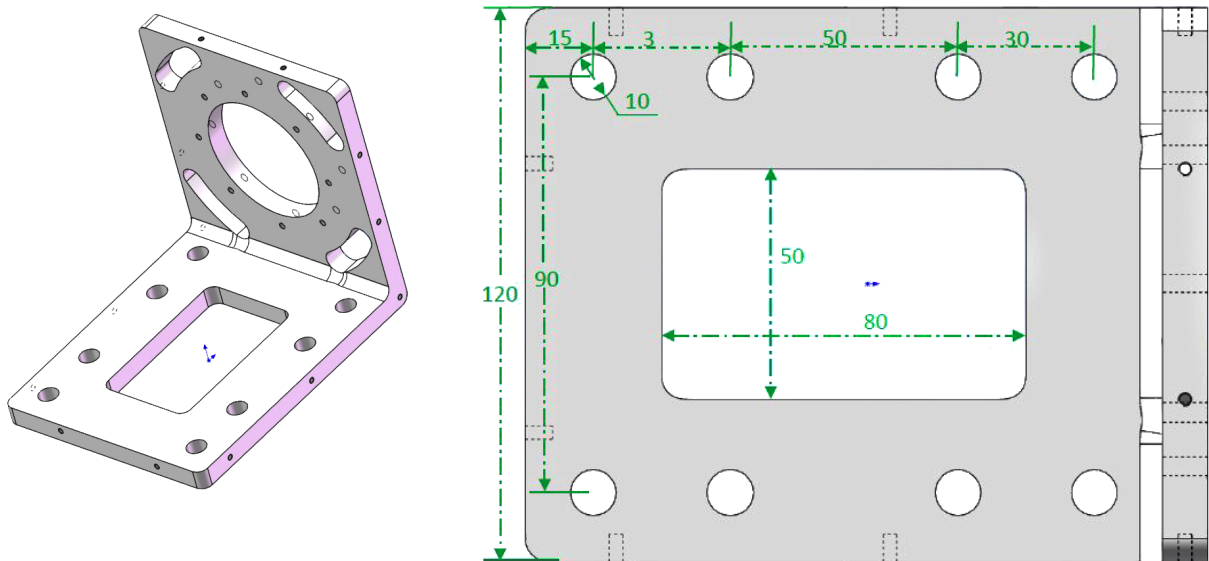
Схема и размеры крепежной пластины редуктора.
